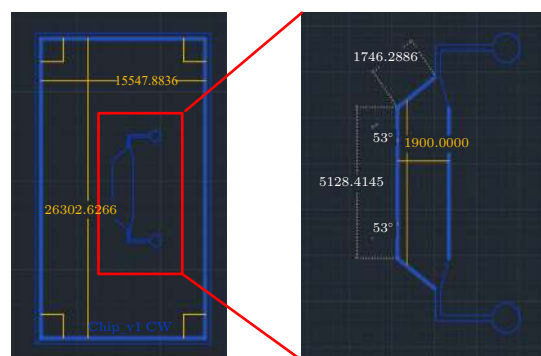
微流控芯片沟道设计 CAD 图及设计参数
